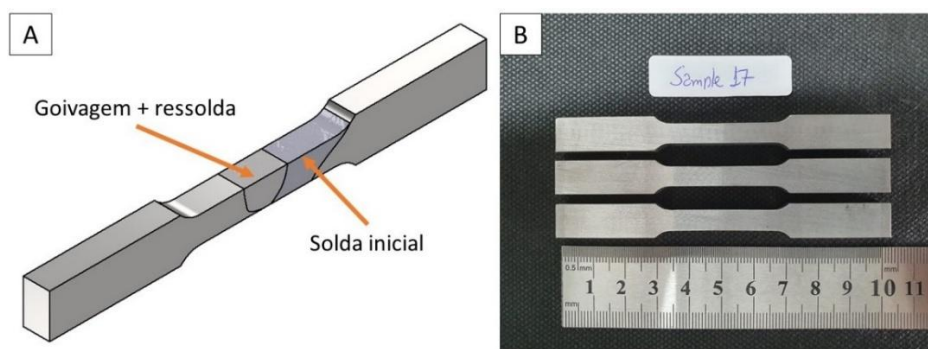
Corpos de provas utilizados para o ensaio de tração, (a) Detalhe da região com solda inicial e a região goivada e ressoldada alocada na área útil e (b) corpos de prova da amostra goivada e ressoldada usinadas em centro de usinagem
